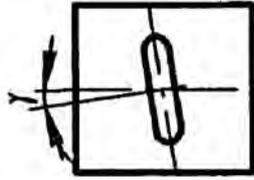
Схемы фрезерования резьбы дисковой фрезой
